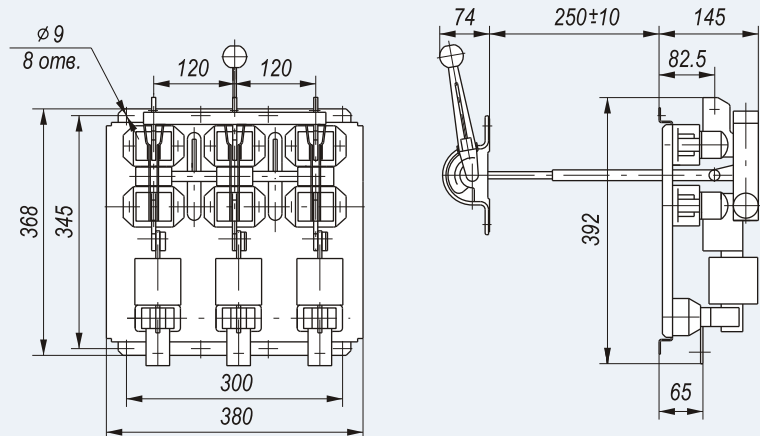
Рубильник с предохранителями на общей плите с центральным приводом РПЦ-6
